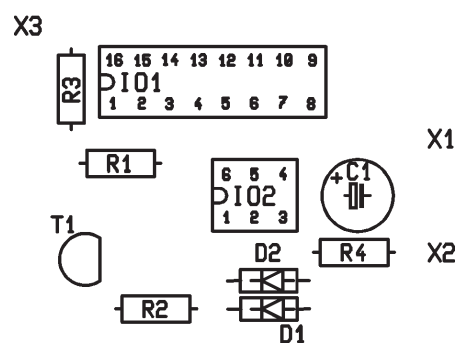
Obrazec plošných spojů generátoru s obvodem UM512-2
